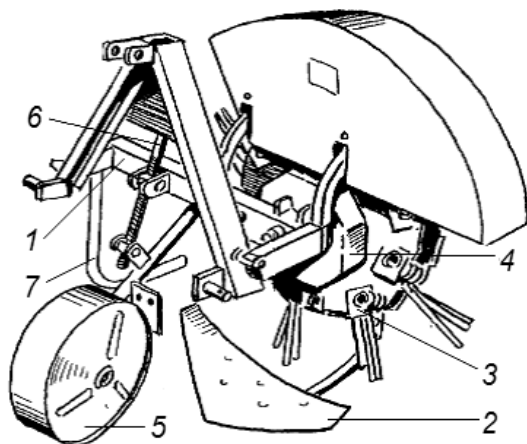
Роторный картофелекопатель: 1 – рама; 2 – лемех; 3 – ротор; 4 – редуктор; 5 – опорно-копирующее колесо; 6 – винтовой механизм; 7 – подставка
